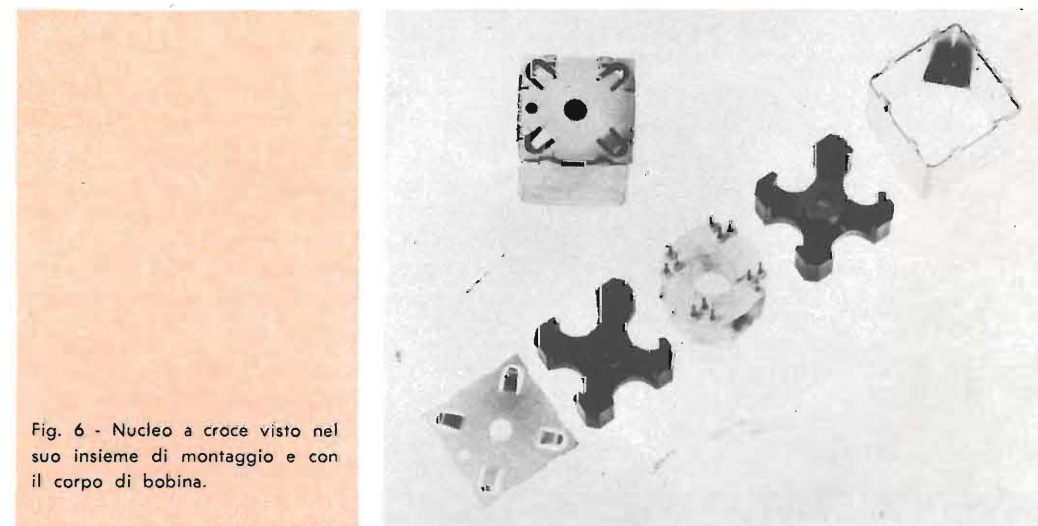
Nucleo a croce visto nel suo insieme di montaggio e con il corpo di bobina.
